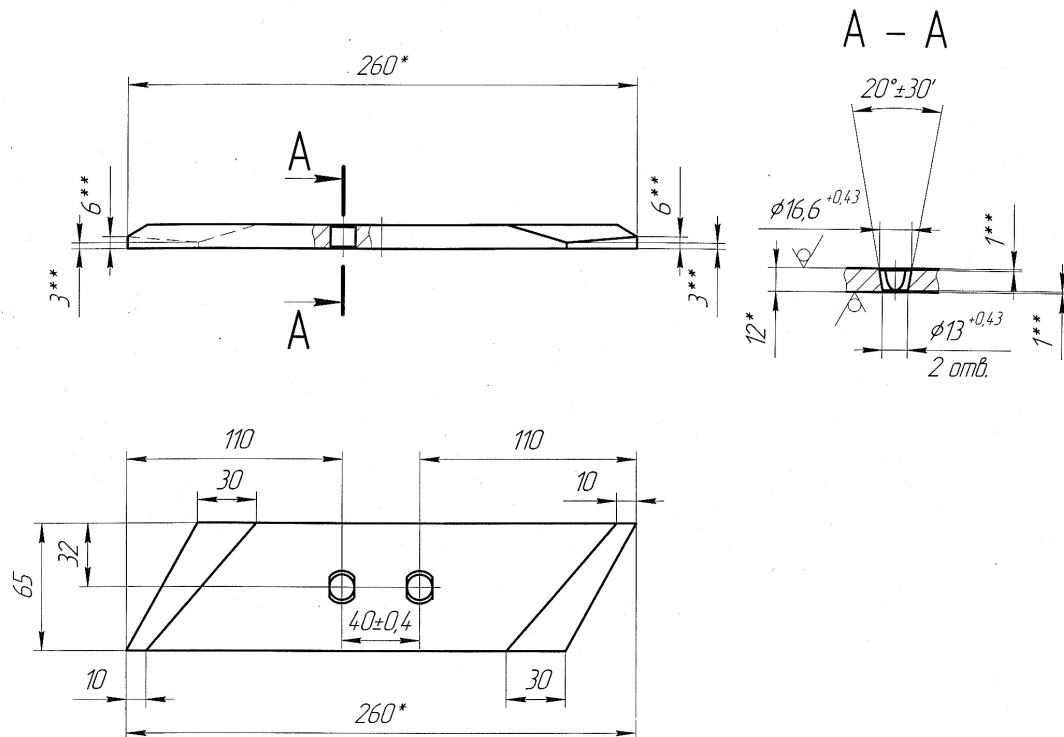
Рабочая деталь почвообрабатывающей техники «долото»
